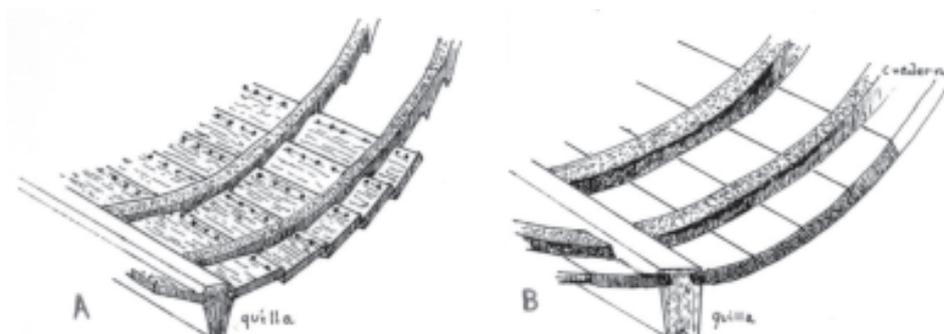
En la figura A vemos un casco construido con planchas de madera solapadas, o en tingladillo. En la figura B vemos un casco de forro liso, o a tope. Las planchas de madera van unidas canto con canto sin solaparse.
